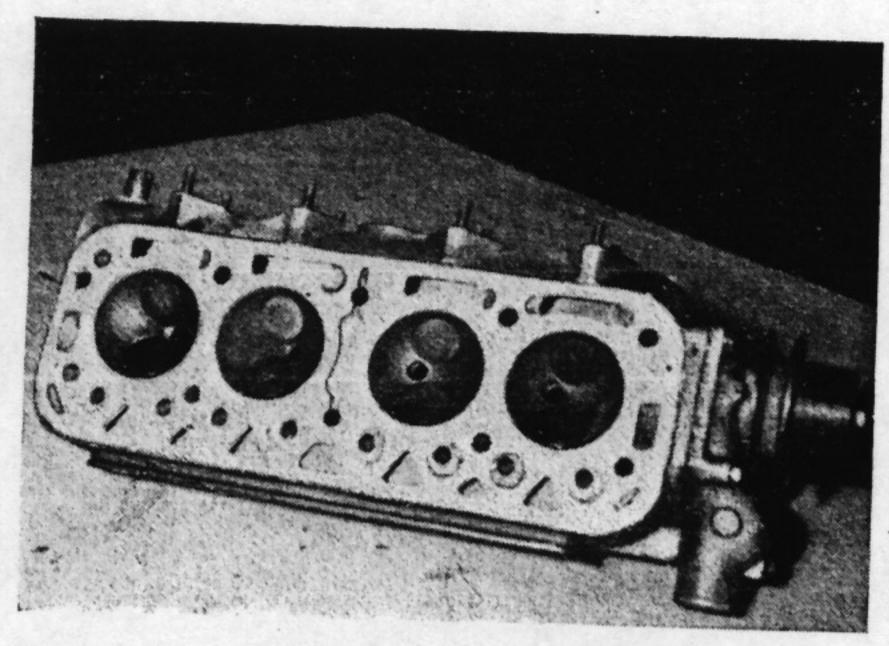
La culasse vue par dessous. Remarquer l'emplacement des bougies très près du centre de la chambre d'explosions.
